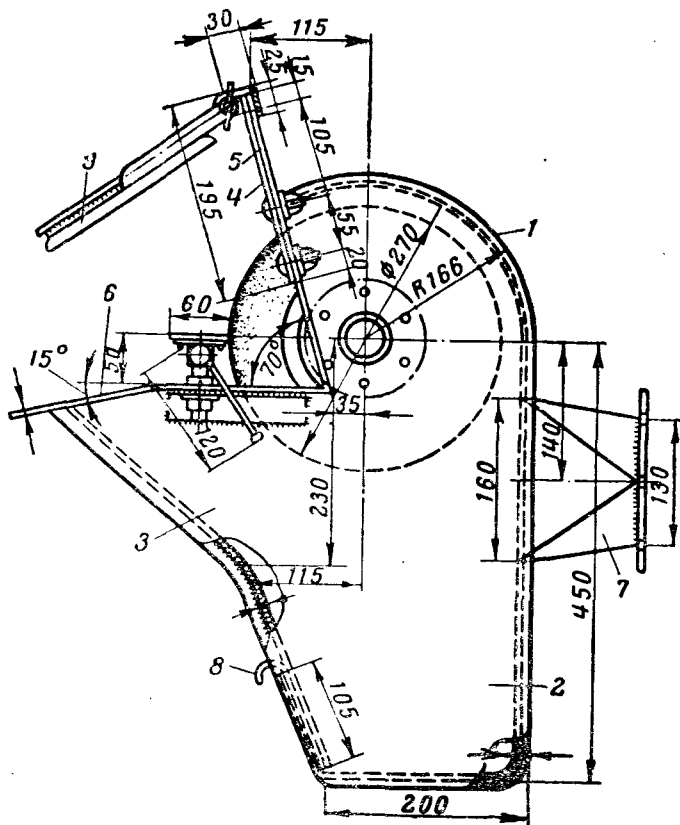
Защитно-обеспыливающий кожух для станков ручной заточки инструмента
